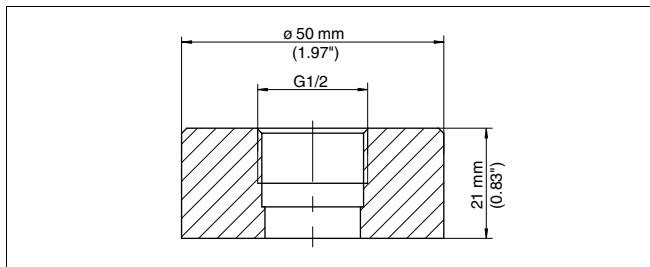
Medidas racor soldado G $\frac{1}{2}$  B según ISO 228-1 - depósito
